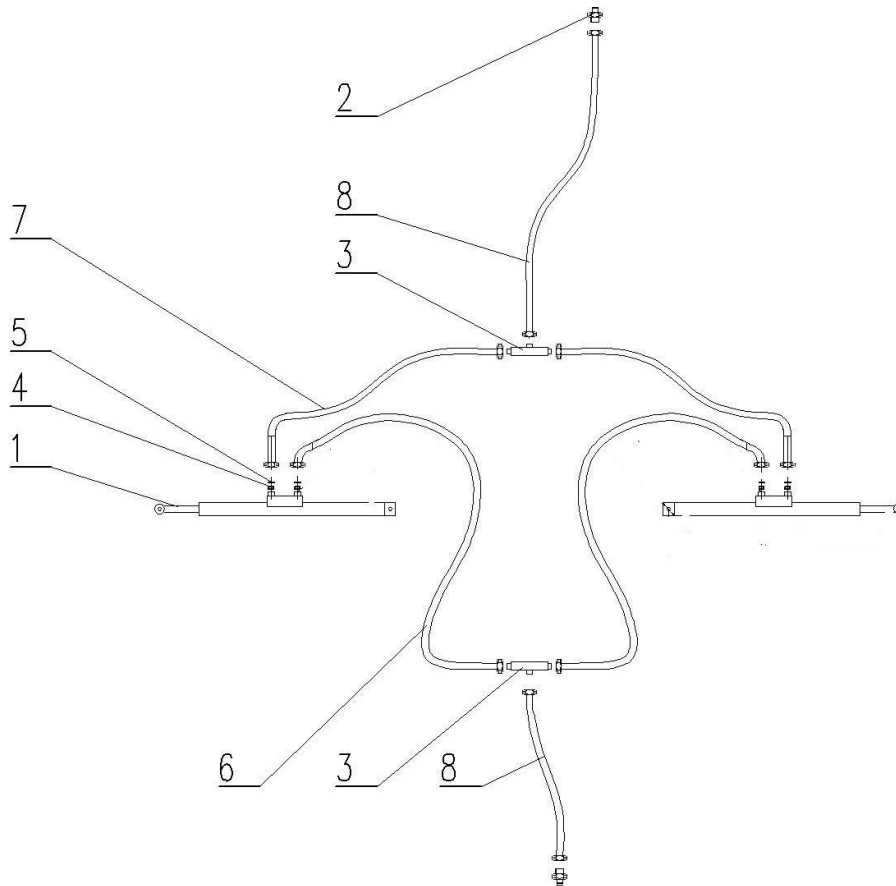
Schema des Hydrauliksystems der Ackerwalze MWC/MWW: 1- Servomotor, 2- Schnellverbinder, 3-T-Stück, 4- Flansch, 5- Kupferunterlegscheibe, 6- Hydraulikleitung 1,2 m, 7- Hydraulikleitung 1,0 m, 8- Hydraulikleitung 2,2 m
